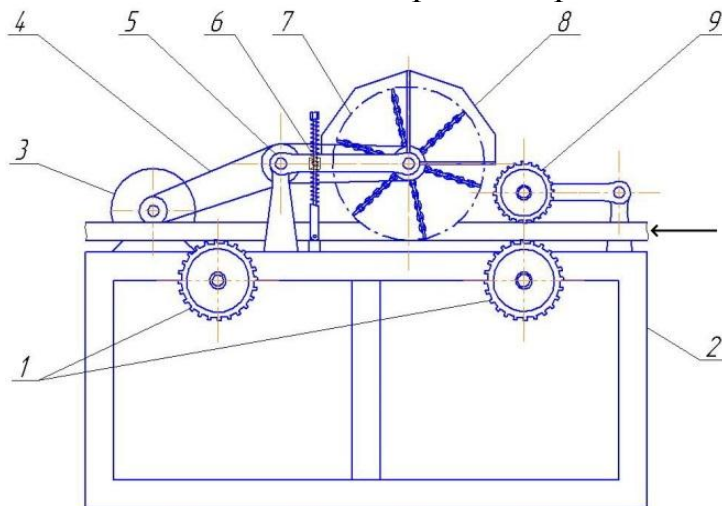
Вид с боку окорочного станка с ЦРО для обработки горбыльных досок: 1 – нижние приводные вальцы системы подачи; 2 – рама станка ЦА - 2; 3- приводной электрический двигатель; 4 – клиноременная передача; 5 – опора с маятниковым механизмом цепового вала; 6 – механизм регулировки высоты окорочного вала; 7- траектория движения звена ЦРО; 8 – защитный экран; 9 – верхний прижимной валец
